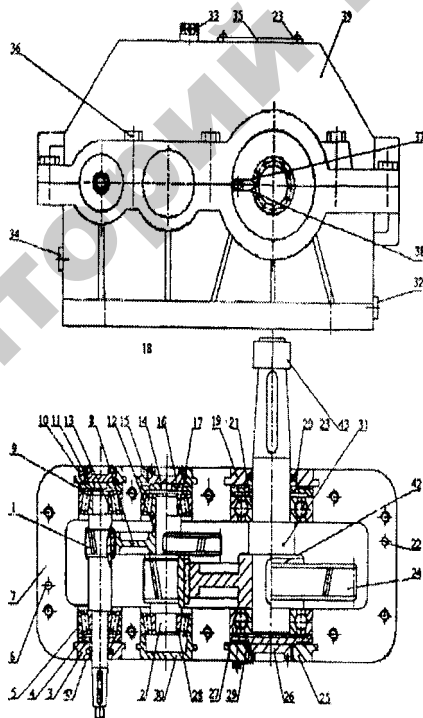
Редуктор цилиндрический двухступенчатый
